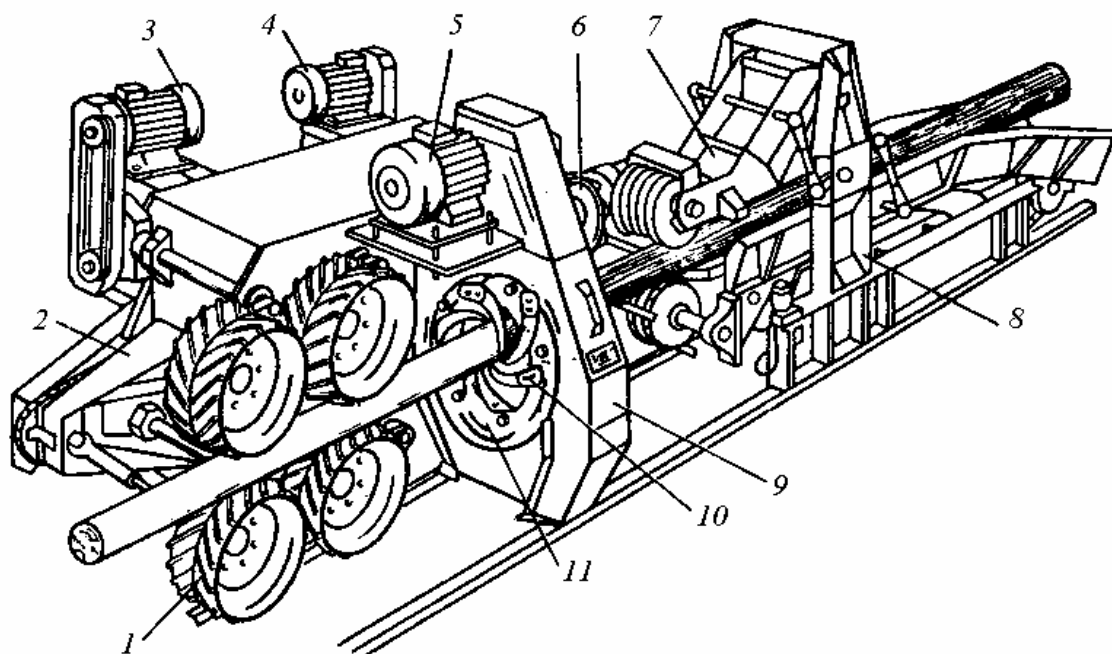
Общий вид роторного окорочного станка: 1, 6 – вальцы приемной и подающей секций механизма подачи; 2 – станина; 3, 4 – привод приемной и подающей секций механизма подачи; 5 – привод ротора; 7 – козырек; 8 – подающий конвейер; 9 – окорочная головка; 10 – коросниматель; 11 – ротор
